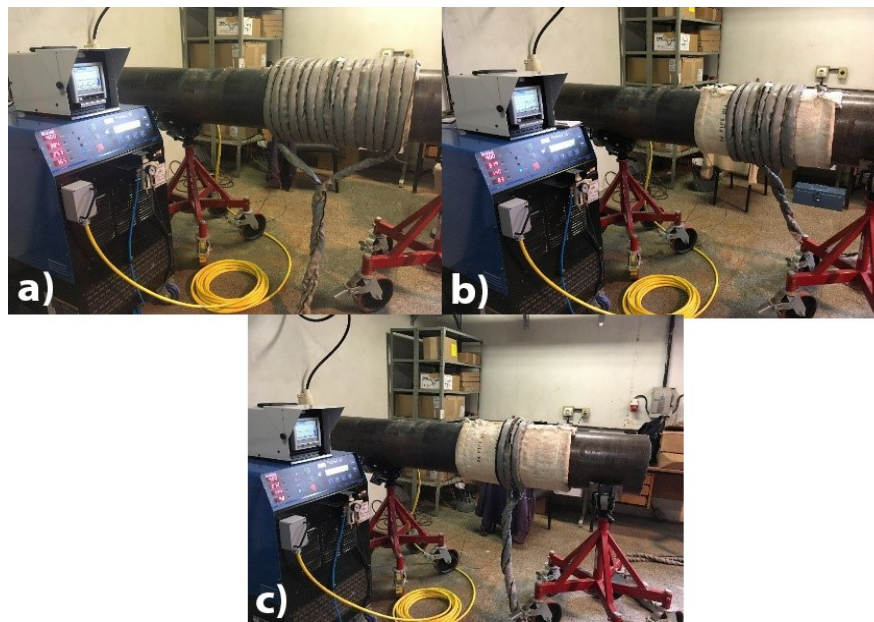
Configurações de bobinas utilizadas nos ensaios com tubo ausente de escoamento interno.
